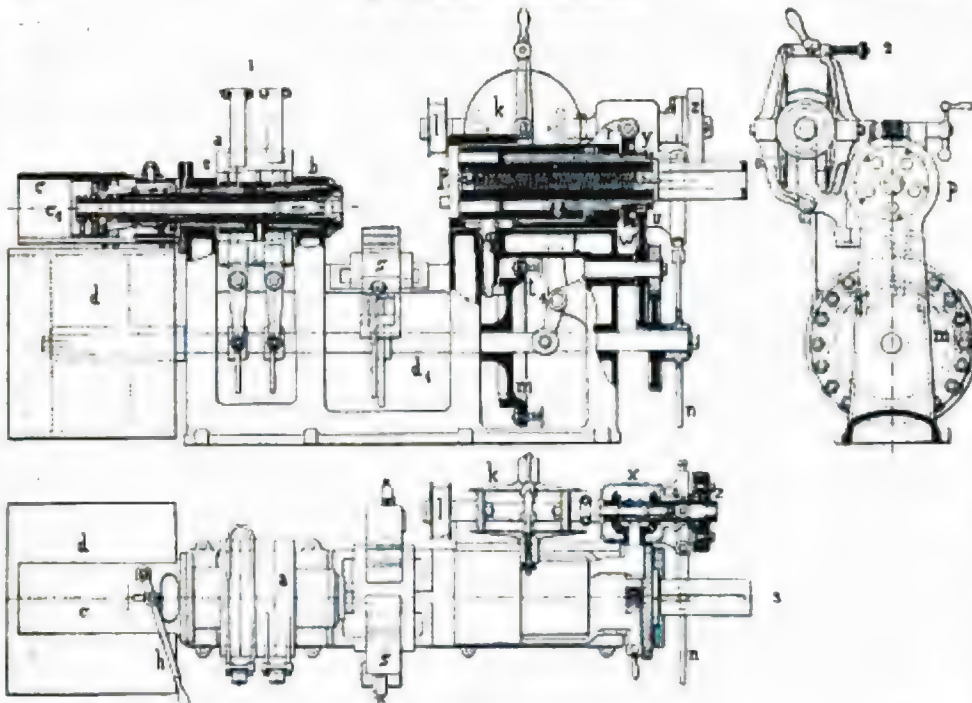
Z. A. Schrauben-Schneidmaschine.
